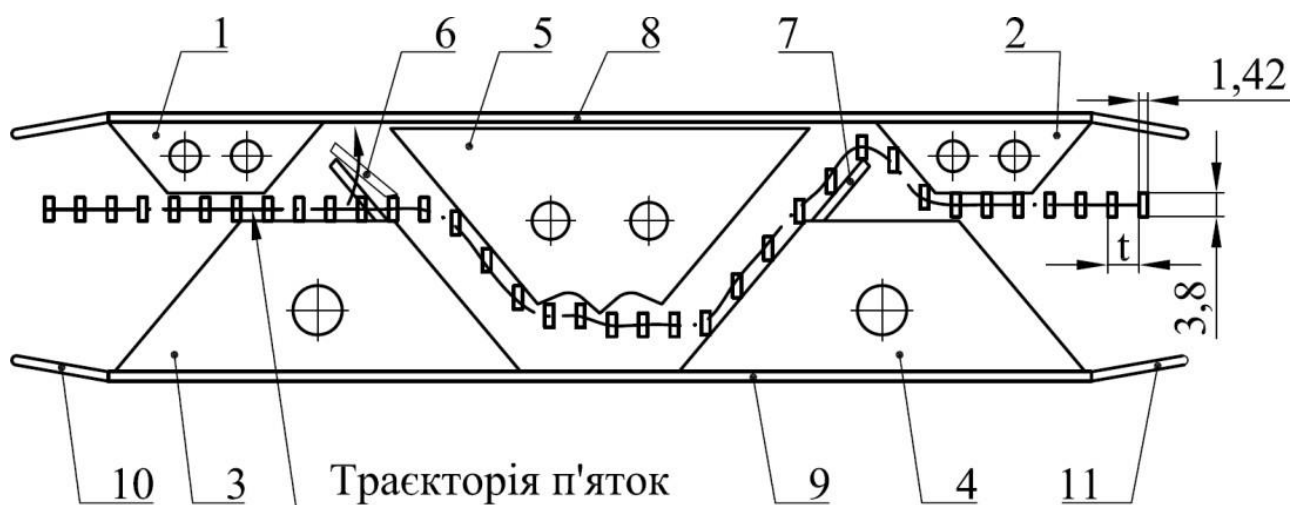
Конструктивна схема (відбитки) замкової дошки в'язальної машини: 1 і 2- верхні клини, що опускають голки при русі каретки вправо(вліво); 3 і 4-підйомні клини; 5-кулірний клин; 6 і 7-поворотні клини; 8-верхня напрямна; 9-нижня напрямна; 10 і 11- ліва та права плоскі пружини.
